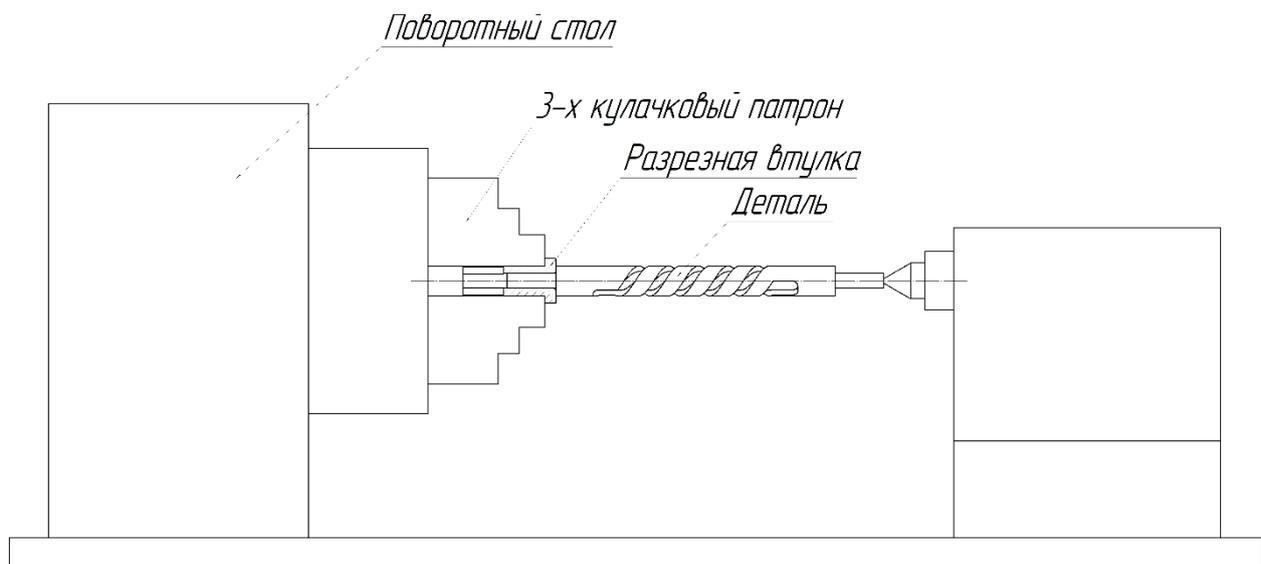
Принципиальная схема установки приспособления на поворотном столе.
